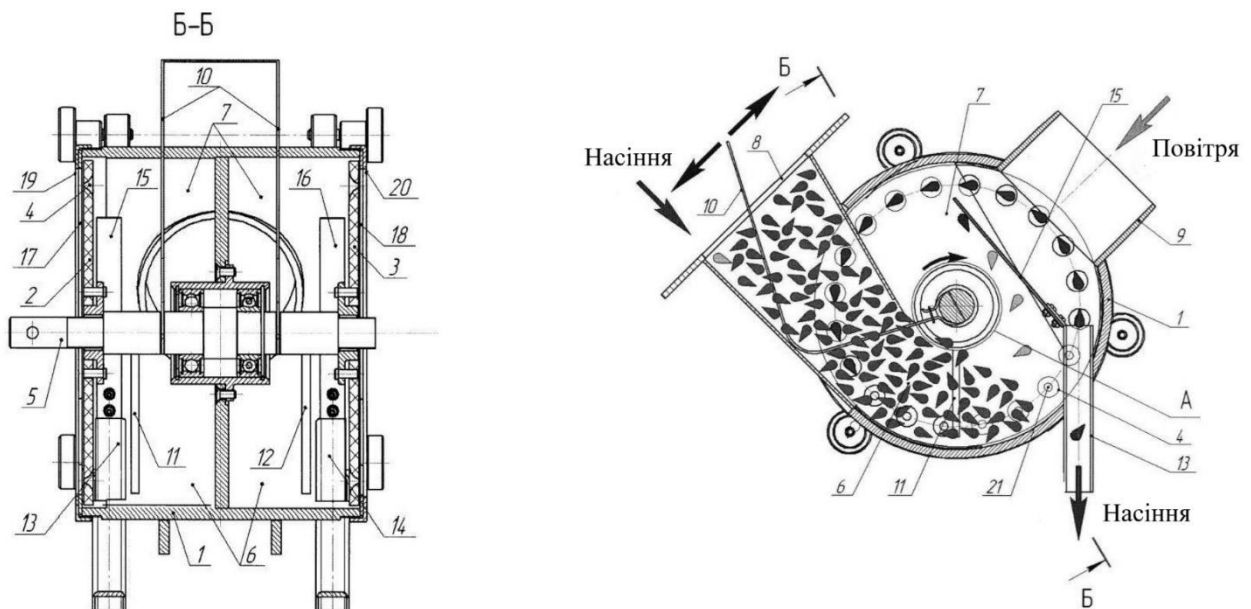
Висівний апарат: 1 – циліндричний корпус; 2, 3 – висівні диски; 4 – отвори; 5 – приводний вал; 6 – насіннєва камера; 7 – камера повітря під тиском; 8 – горловина; 9 – канал подачі повітря; 10 – склепінювач; 11, 12 –
